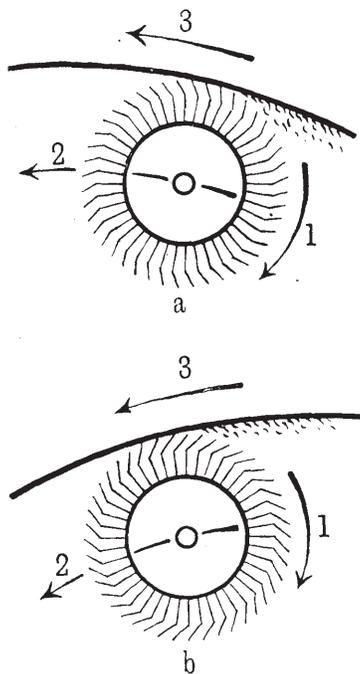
Strich- und Gegenstrichwalzen der Gessnerschen Rauhmachine.
